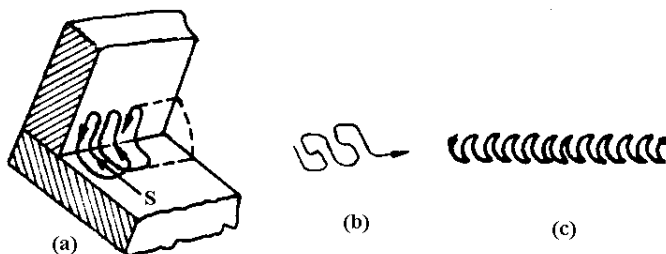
Movimentação do eletrodo em soldas de ângulo, (a) Movimento do eletrodo para um único passo, (b,c) movimento do eletrodo para passo de enchimento para múltiplos passos.
